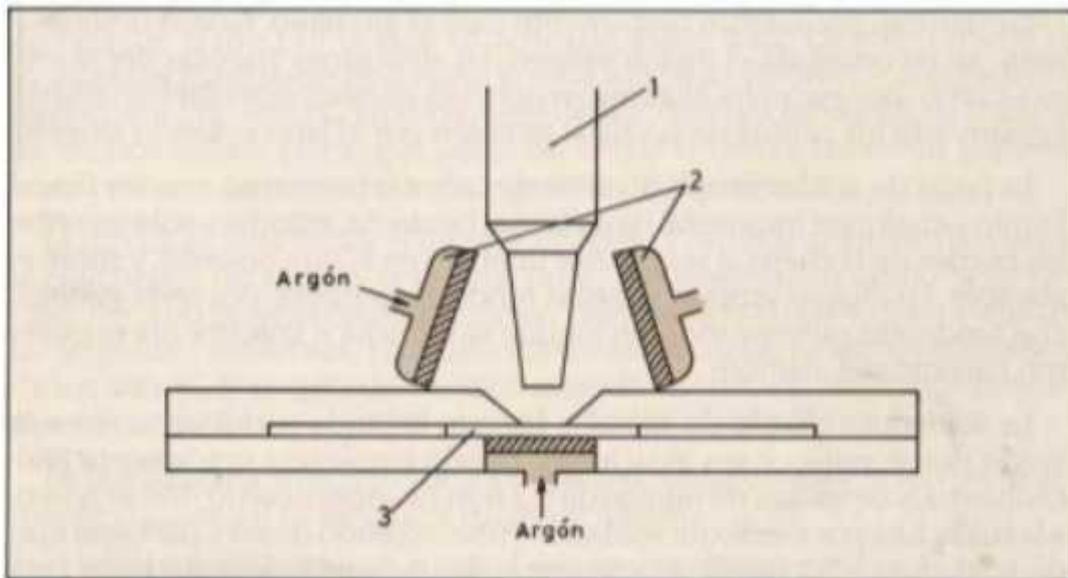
Soldadura del titanio con protecciones laterales e inferior: 1) Pistola para soldar; 2) gas protector; 3) piezas a soldar
